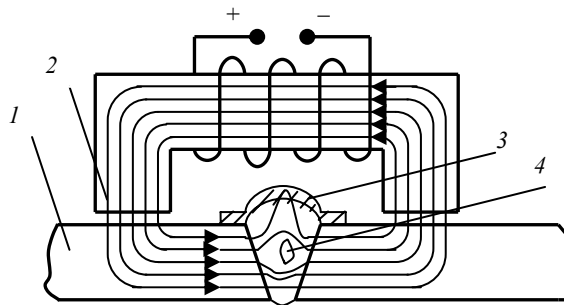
Схема проведения магнитографического контроля сварного шва:
